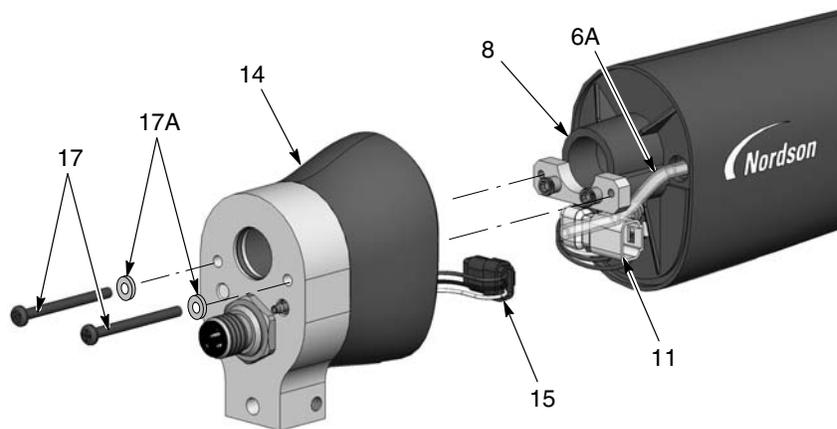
Desmontagem de pistola com barra de suporte 1 de 3
